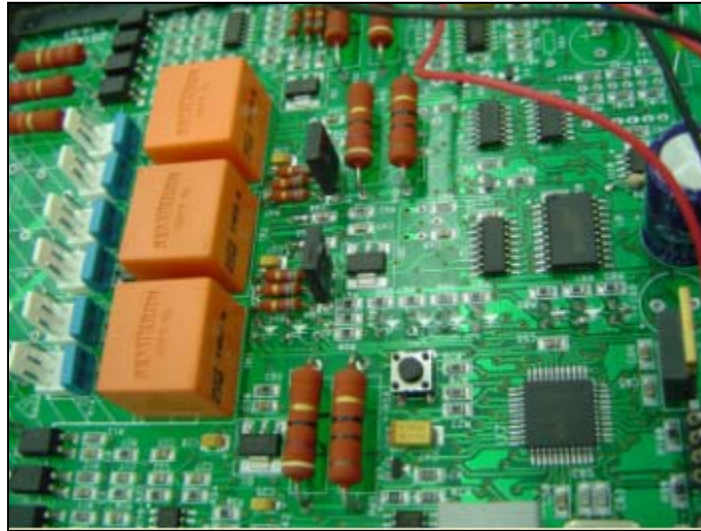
PLACA ELETRÔNICA COM COMPONENTES SMD E PTH
